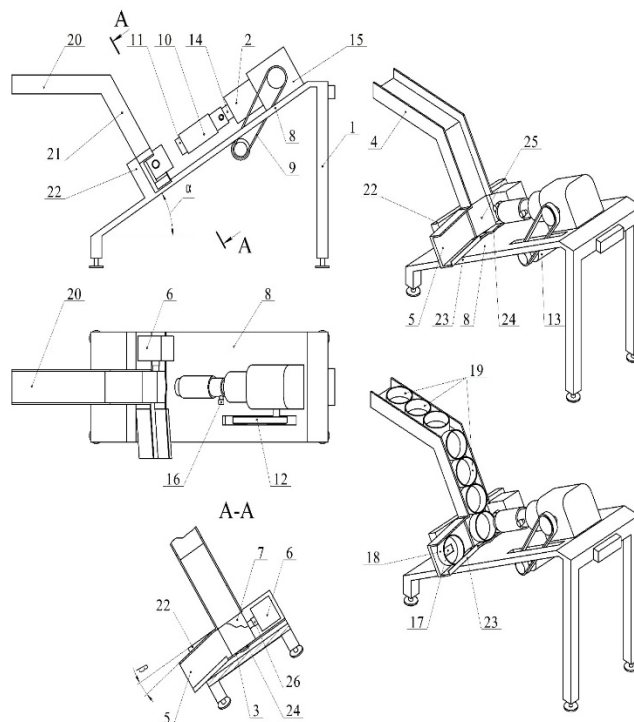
Устройство для маркировки дна металлических консервных банок:
